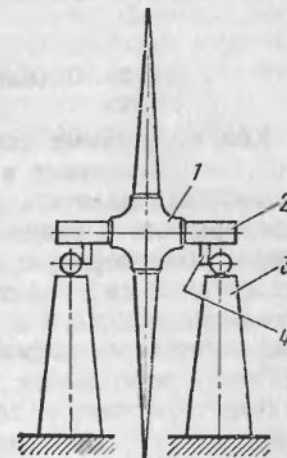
Схема установки для статической балансировки воздушных винтов
